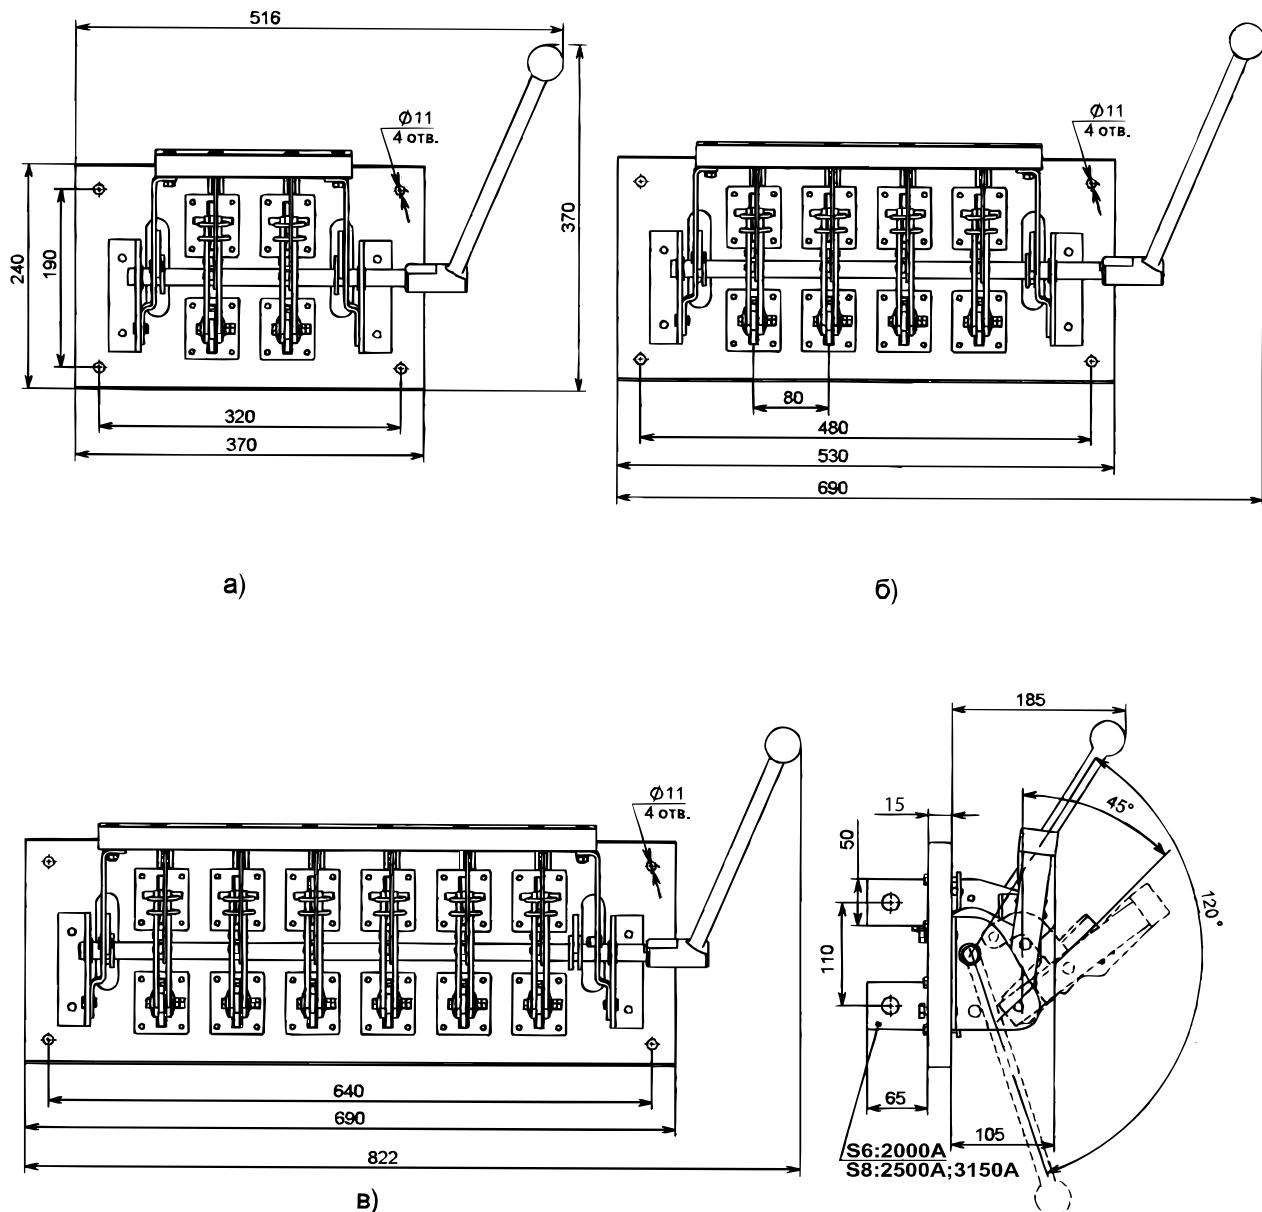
Разъединитель РЕ19 с боковой рукояткой, заднего присоединения шин
